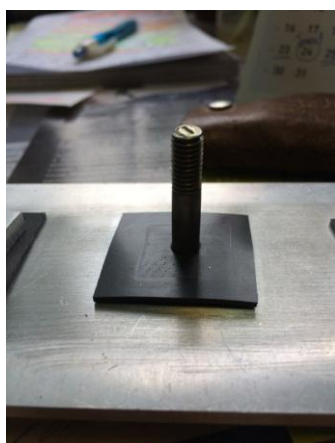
Образец материала марки ВТП-1В, извлеченный из болтового соединения
